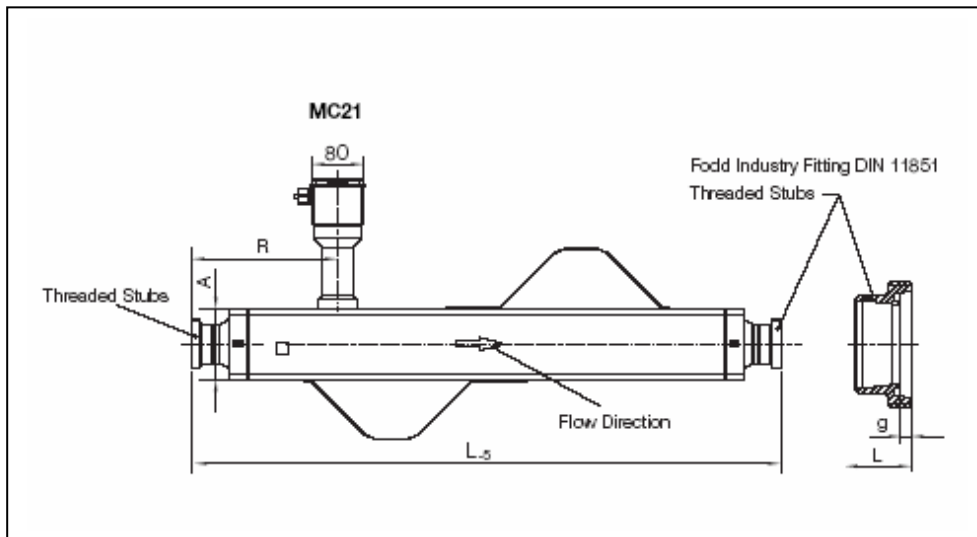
/29 Молочная гайка (Food Industry Fitting размеры от „G“ до „K“, DIN 11851)
